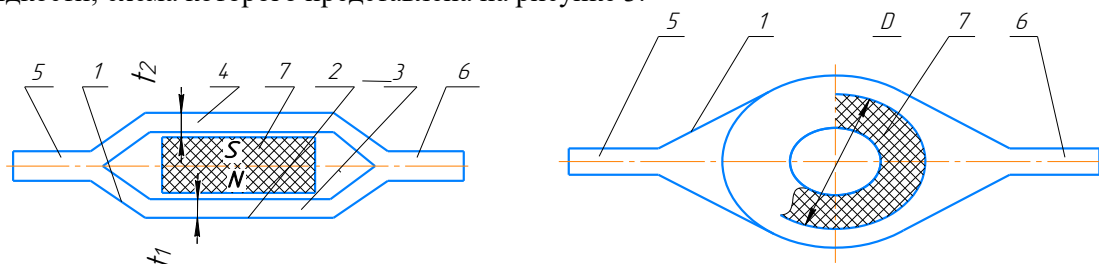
Устройство для магнитной обработки жидкости: 1 – корпус; 2 – центральная часть корпуса; 3 и 4 – цилиндрические полости; 5 – входной штуцер; 6 – выходной штуцер; 7 – постоянный кольцевой магнит
